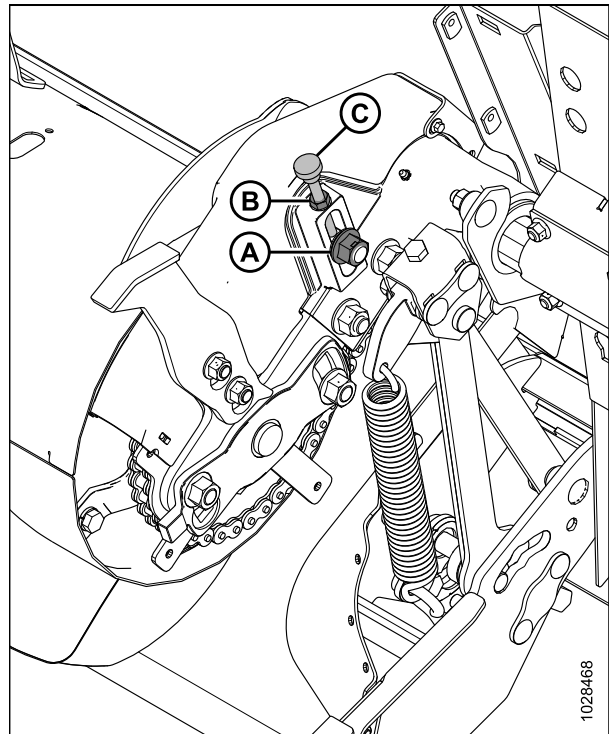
Левая сторона привода шнека - вид спереди
